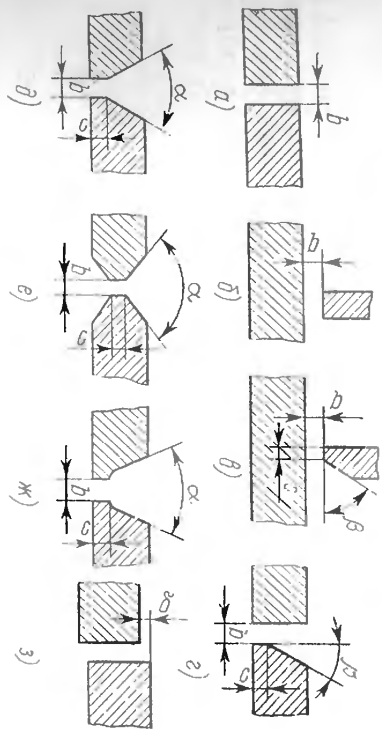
Конструктивные элементы кромок, подготовленных под сварку:
